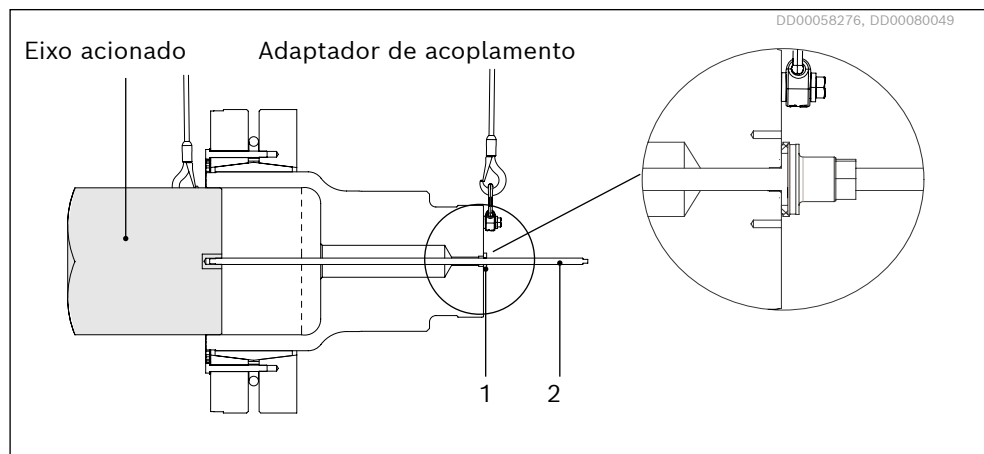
Montagem do adaptador de acoplamento no eixo acionado com a ferramenta de montagem.
